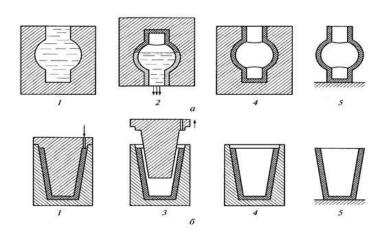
Способы шликерного литья: а—сливной; б—наливной; 1—заливка шликера; 2—слив—излишнего шликера; 3—разъем формы; 4—подвалка;
